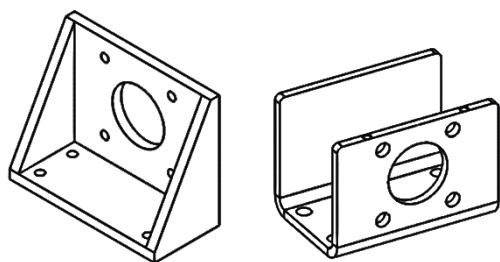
Piastre supporto motore, a sinistra quella stampata e a destra quella ottenuta per piegatura
